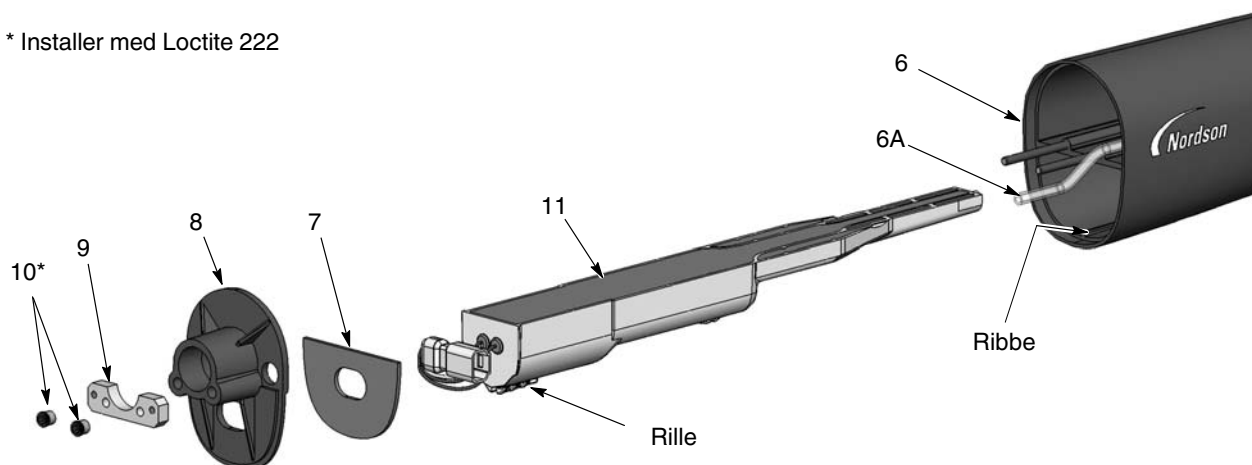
Adskillelse af pistol til montering på holdestang 1 af 3
